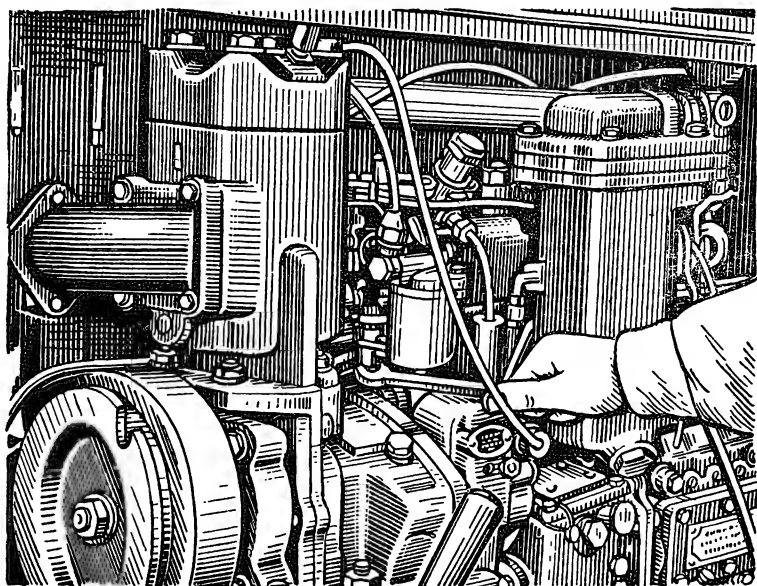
Спуск отстоя из поплавковой камеры карбюратора через спускной штуцер
